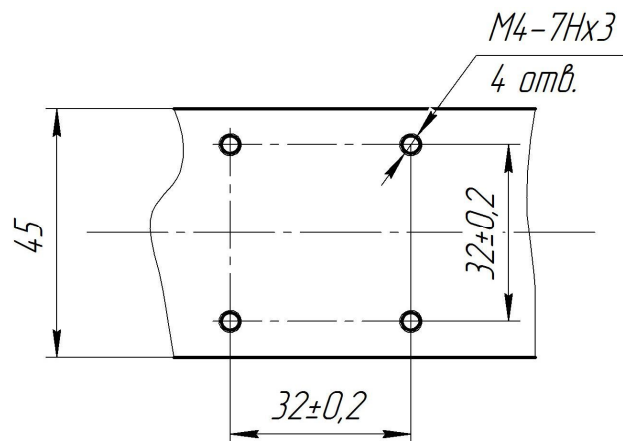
Присоединительные размеры под установку датчика контроля вибрации для КМВГ 40-25-150Е
